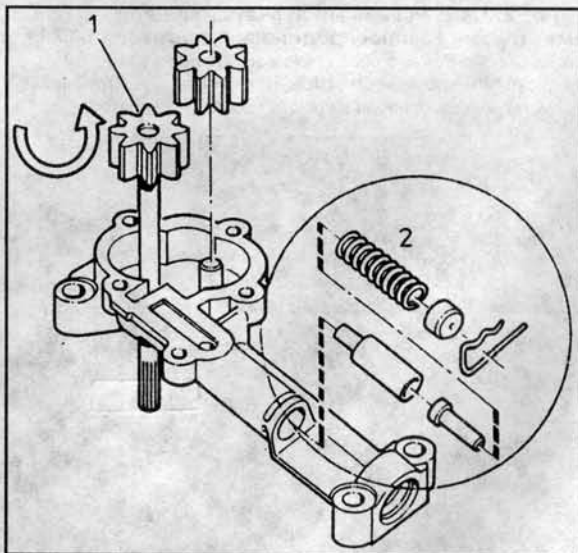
Масляный насос и редукционный клапан двигателя В172
